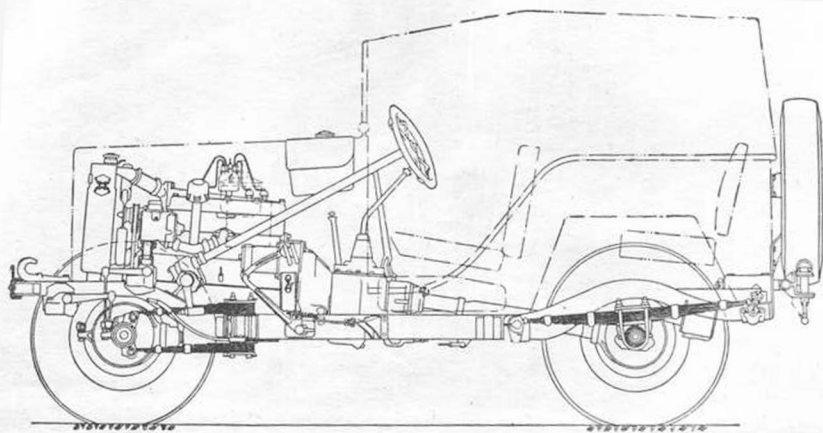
Автомобиль ГАЗ-67Б (чертеж общего вида сбоку).
